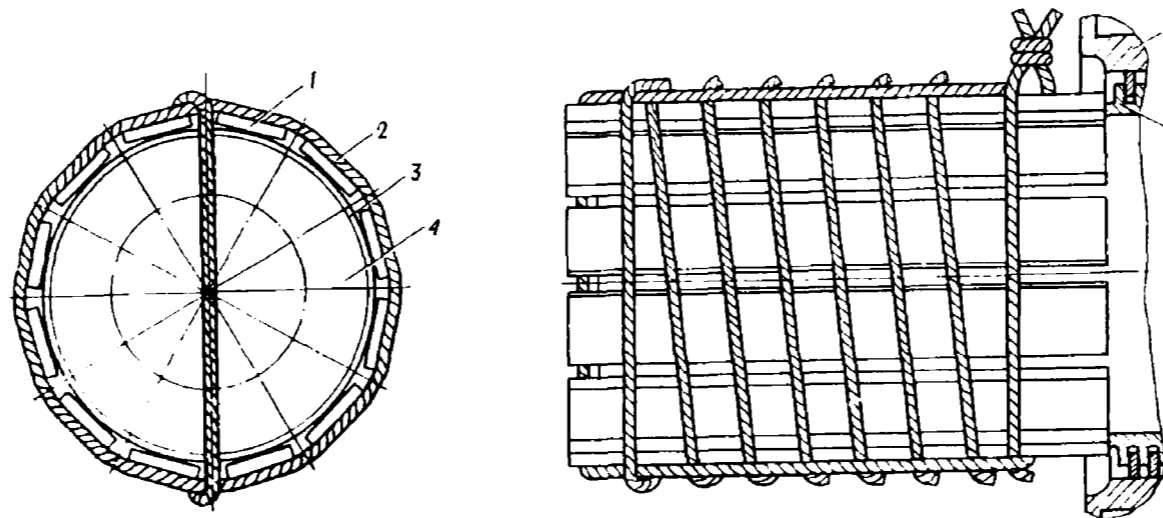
Упаковка носка коленчатого вала дизелей типа В-2:
